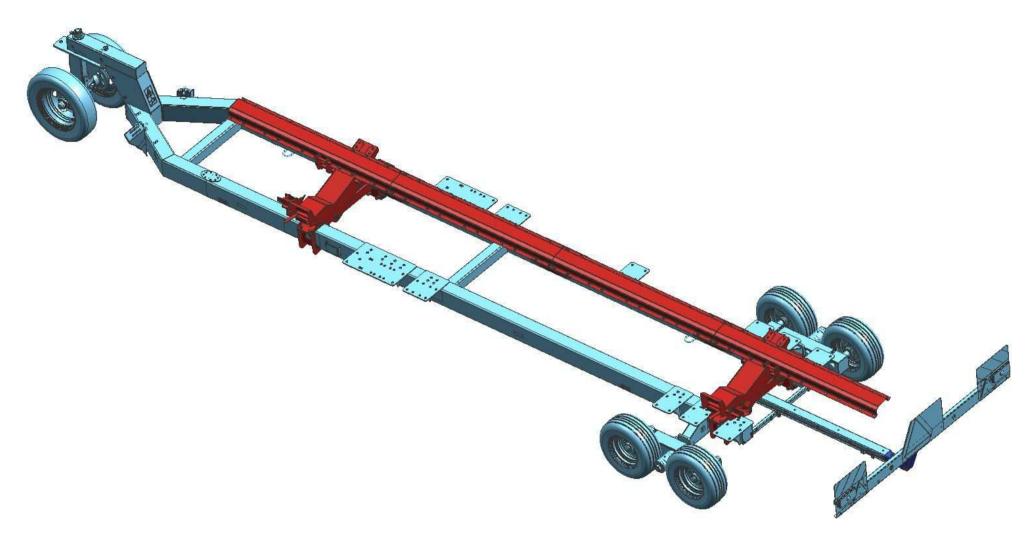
Приспособление для перемещения адаптеров ППА-4000 "Uni Cart 4000" для RSM SS-560, RSM SS-650 (с комплектом для транспортировки SS-780.13.00.000)
